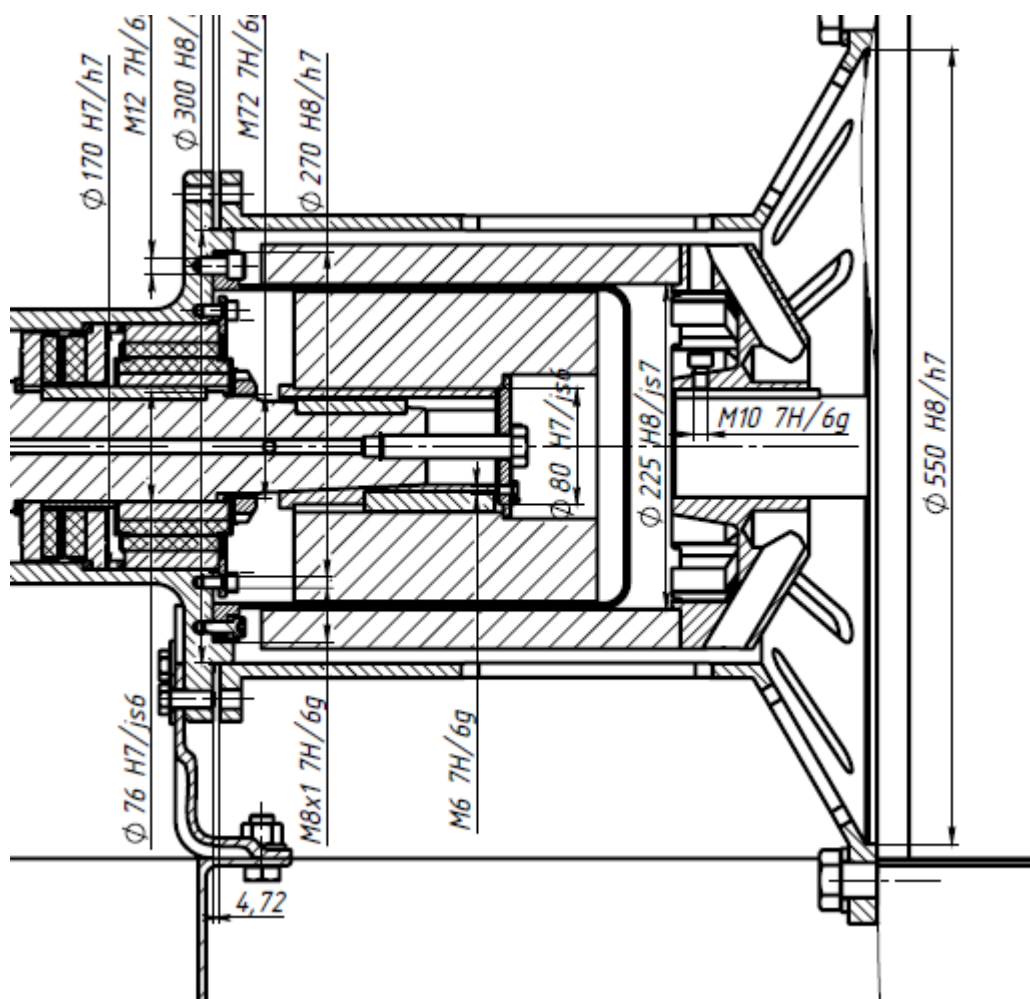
Конструкция внешней магнитной полумуфты и ее защитного кожуха
